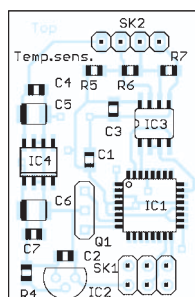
Schaltung der Baugruppe für die Pumpen- und Ventilsteuerung
